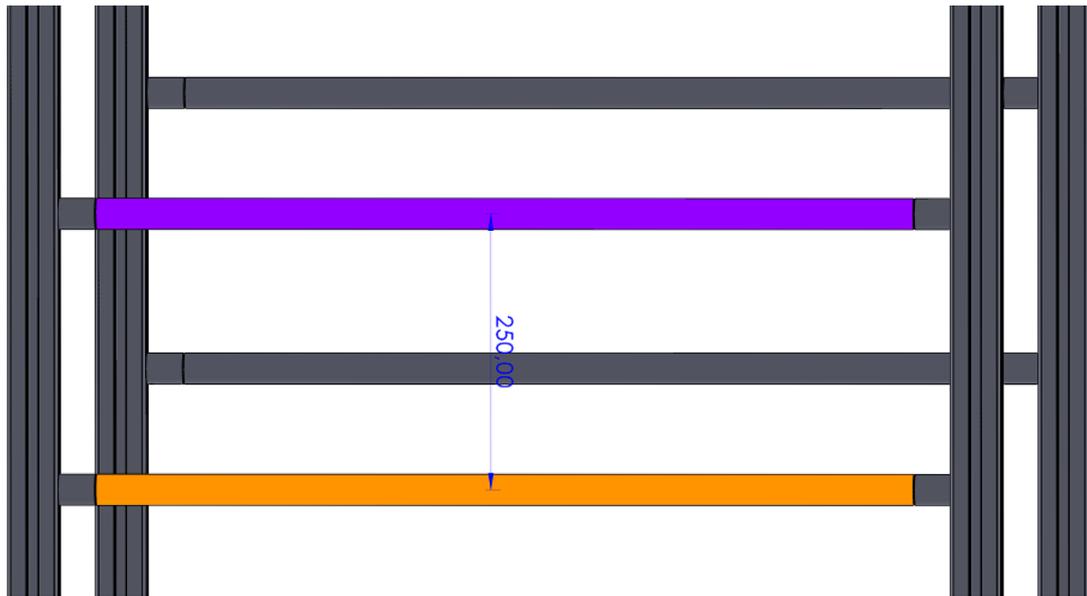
TRAVESAÑOS ESTRUCTURA LAVADORA. (ELABORACIÓN PROPIA)
